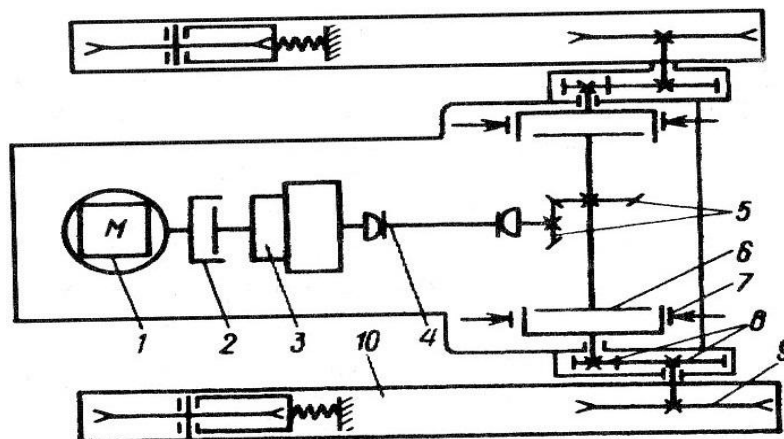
Схема механической трансмиссии гусеничного трактора: 1 – двигатель; 2 – муфта сцепления; 3 – коробка передач; 4 – соединительный вал; 5 – главная передача; 6 – бортовой фрикцион; 7 – тормоз; 8 – бортовой редуктор; 9 – ведущая звездочка; 10 – гусеница
